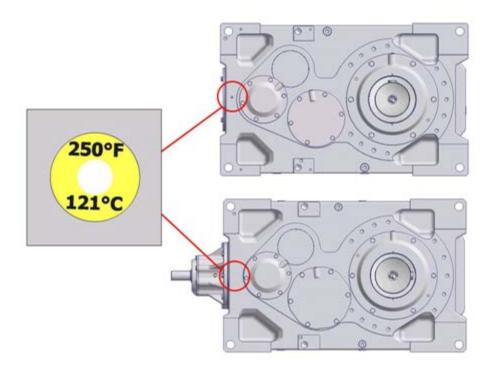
Положение наклейки-индикатора температуры на корпусе цилиндрического или конического редуктора
